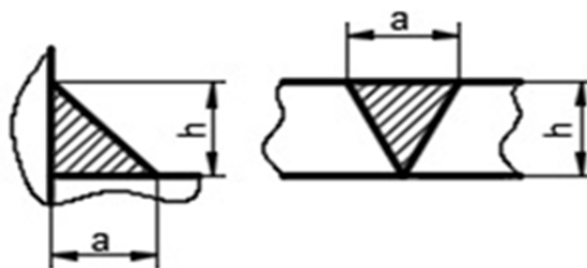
Сварочный шов: a – основание шва; h – высота шва
